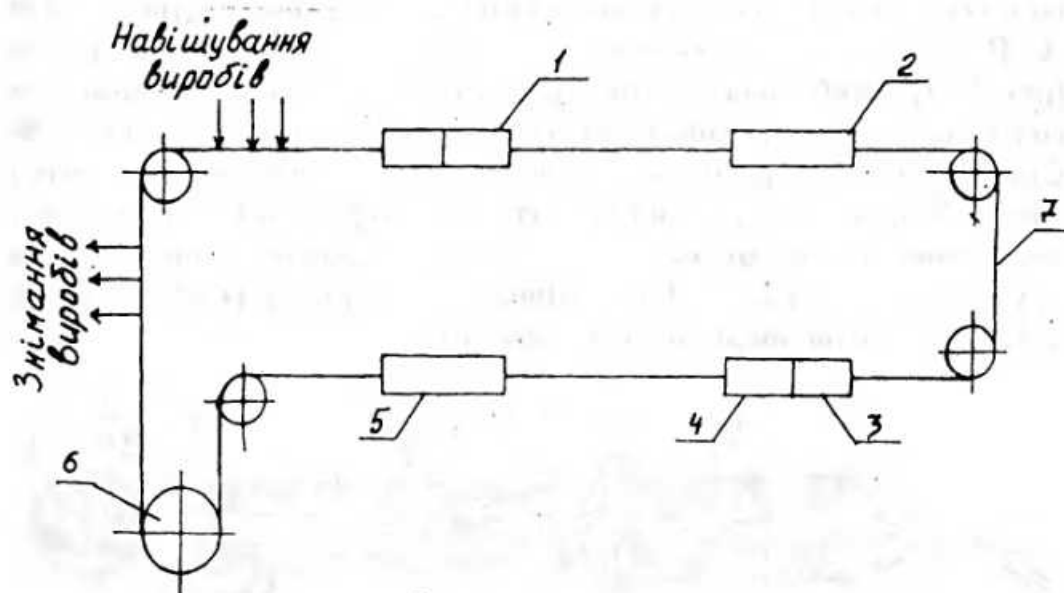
Схема фарбування виробів методом струменевого обливання: 1-мийний агрегат; 2-сушильна камера; 3- камера струменевого обливання; 4 - паровий тунель; 5 - сушильна камера; 6 - приводна станція; 7 -конвеєр
